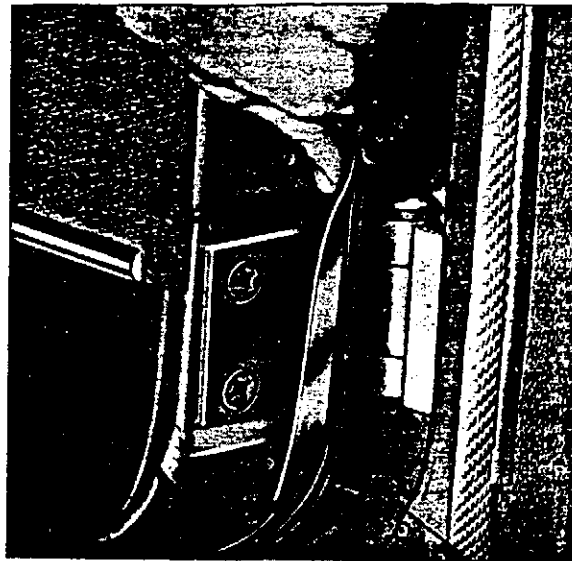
Blech über dem Scharnier, früh. Ausf.
